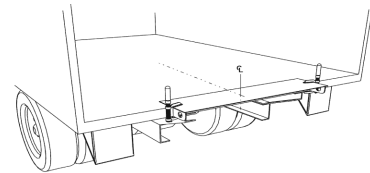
Montagevorrichtung mit Schraubzwingen, Schrauben oder per Punktschweißung an der Hecktraverse befestigen
